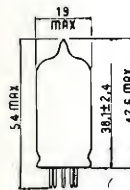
Dimensioni di ingombro della valvola IS5.
